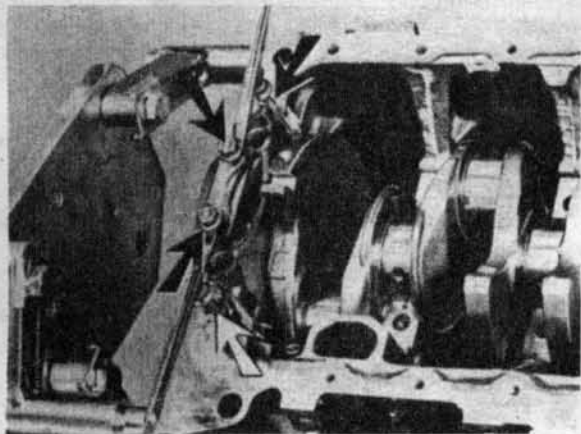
Способ снятия крышки 1-го коренного подшипника коленвала
